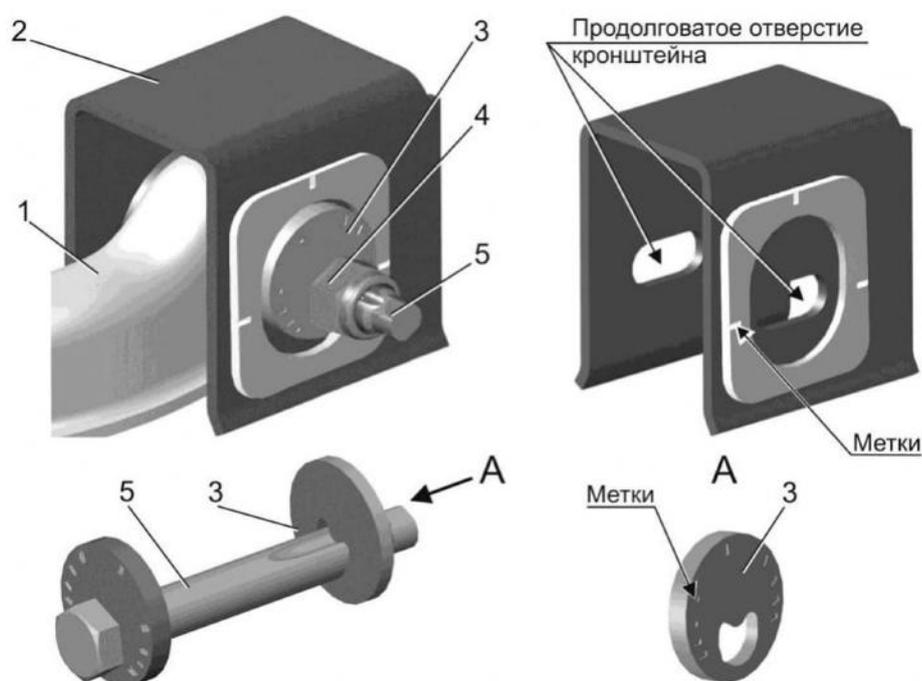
Устройство для регулировки углов установки колес: 1 – верхний рычаг подвески; 2 – кронштейн верхнего рычага подрамника; 3 – шайба эксцентриковая; 4 – гайка; 5 – регулировочный болт в сборе с эксцентриковой шайбой
